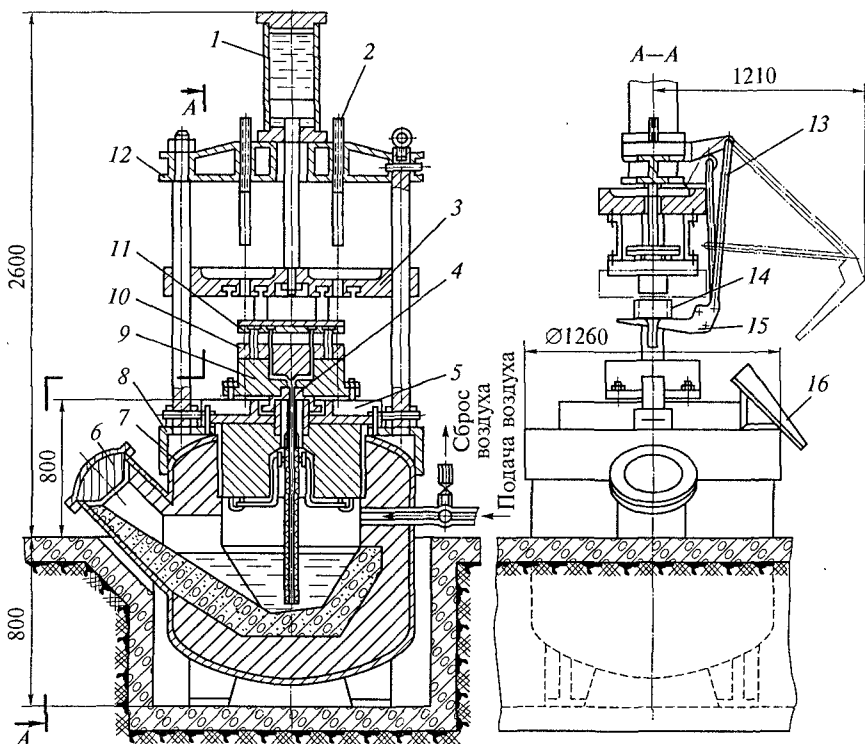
Установка литья под низким давлением для получения отливок из алюминиевых сплавов:
